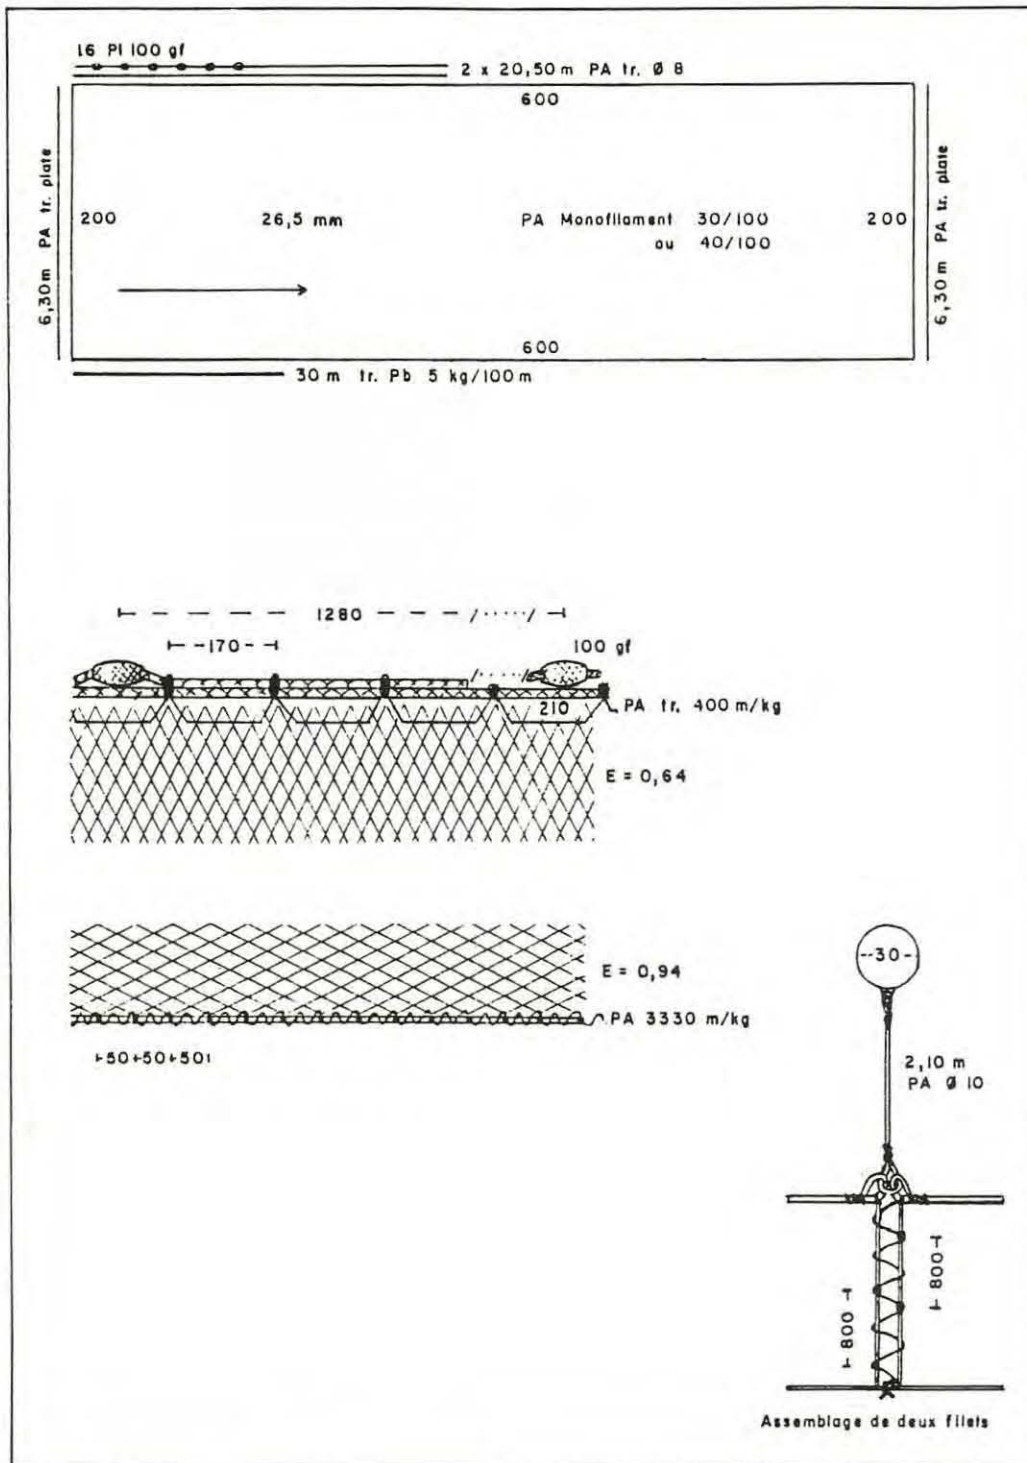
Plan d'un filet maillant dérivant ou roie pour la pêche du hareng.
